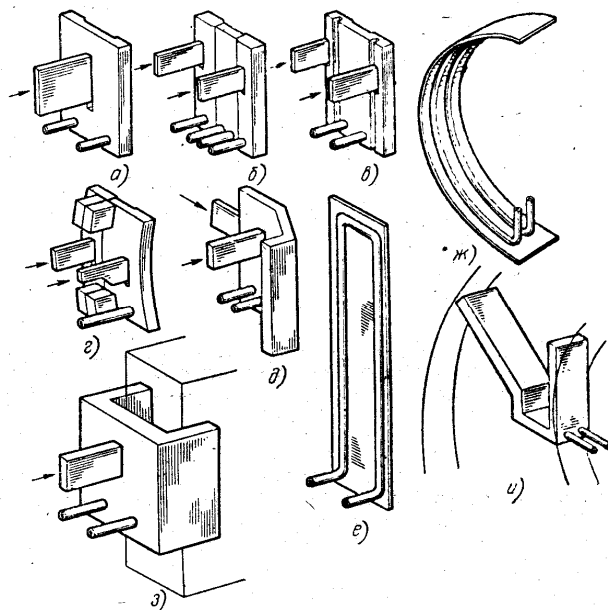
Подвижные и неподвижные формирующие устройства для электрошлаковой сварки (ползуны):
